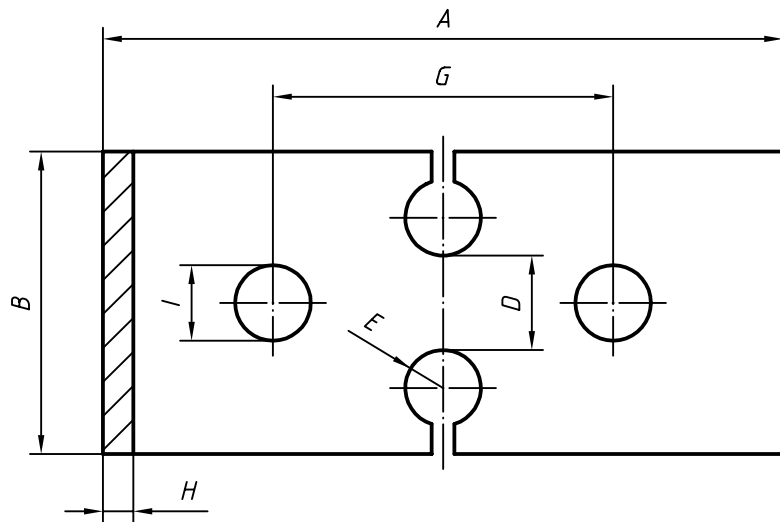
Éprouvette de traction usinée, de type A (pour  $e < 25$  mm)
